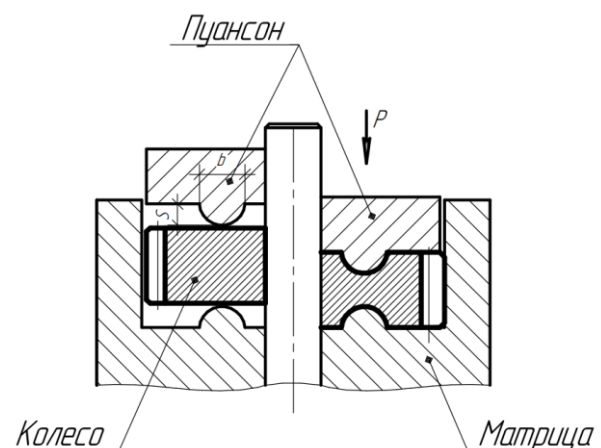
Схема восстановления зубчатого колеса выдавливанием
